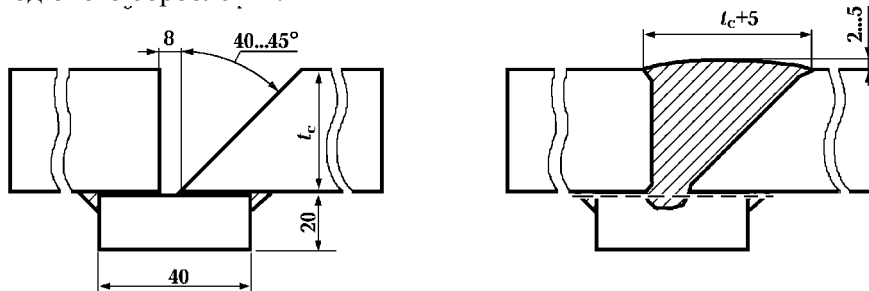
Зварні з'єднання листового прокату для випробувань на зварюваність
